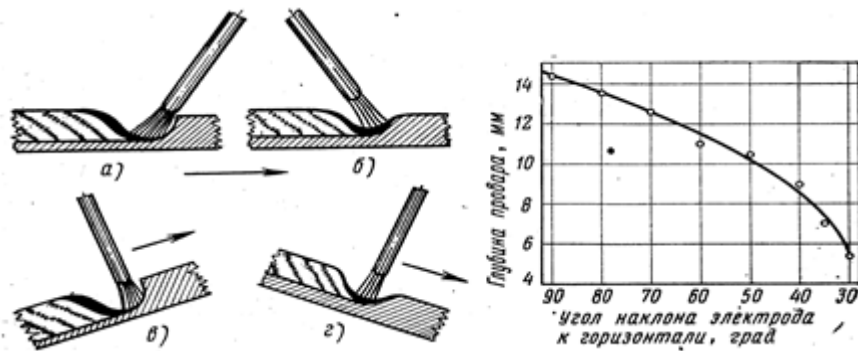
Положение электрода и изделия в пространстве: а-«сварка углом назад»; б-«сварка углом вперед»; в-«сварка на подъем»; г-«сварка на спуск»
